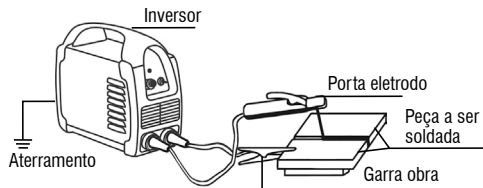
Montagem dos cabos de solda para soldagem de Eletrodo Revestido (MMA)
